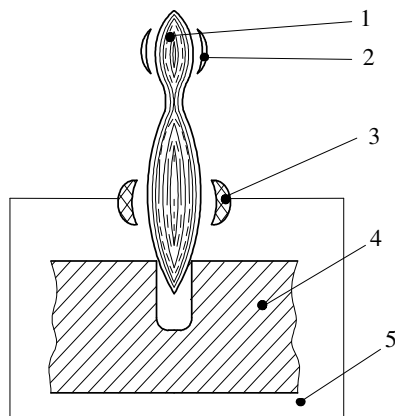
Schema de principiu la prelucrarea dimensională cu fascicul de electroni:
